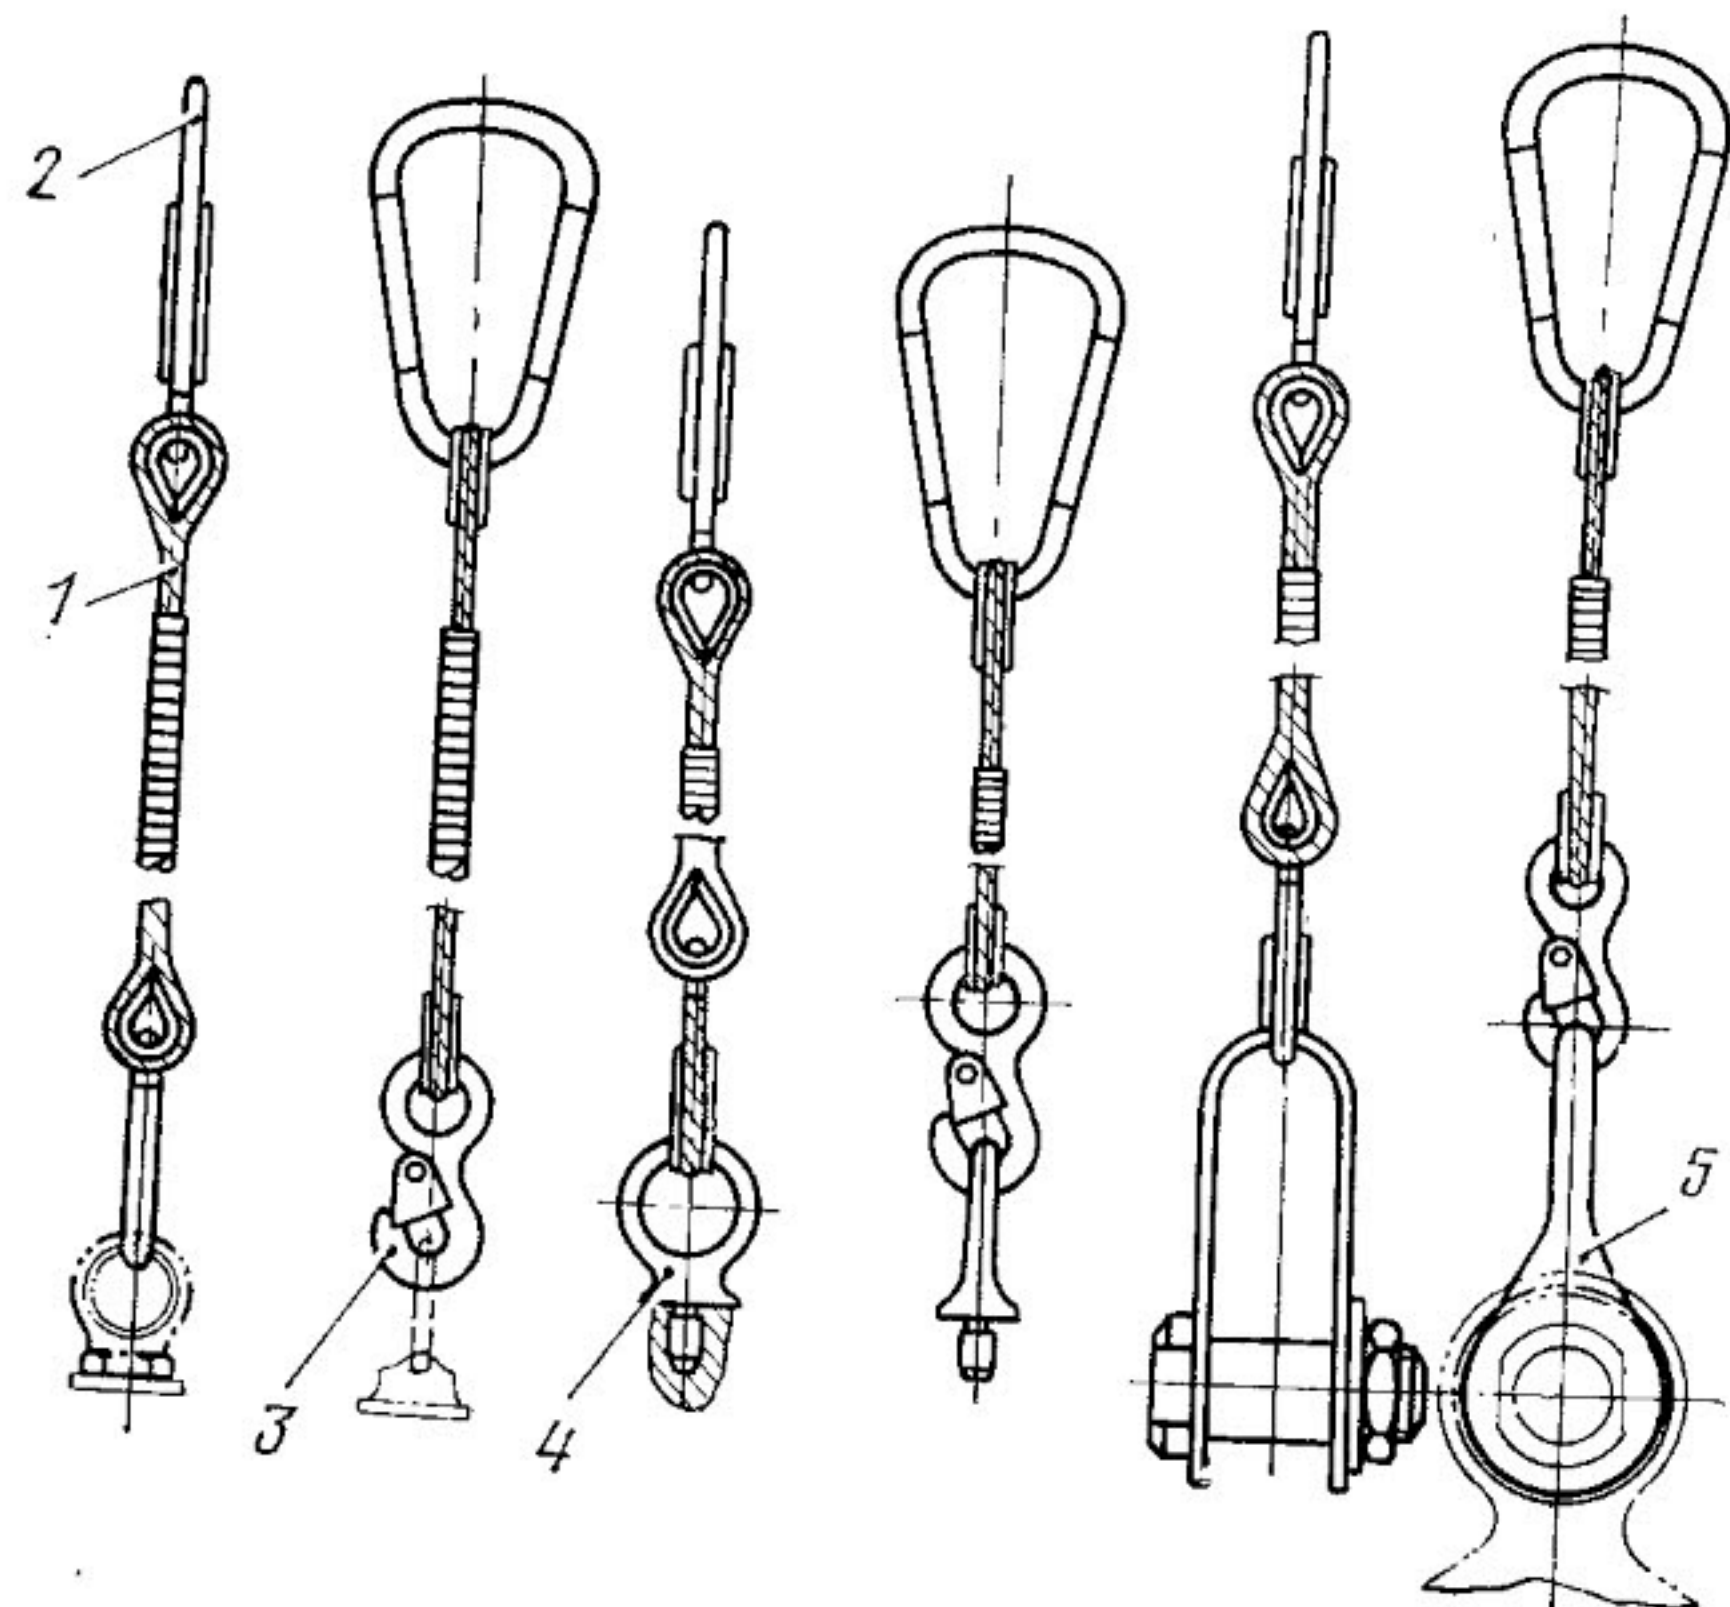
Подвеска для подъема хвостового редуктора, промежуточного редуктора и бустеров БУ32А и БУ33А и рулевых приводов РП-28:
